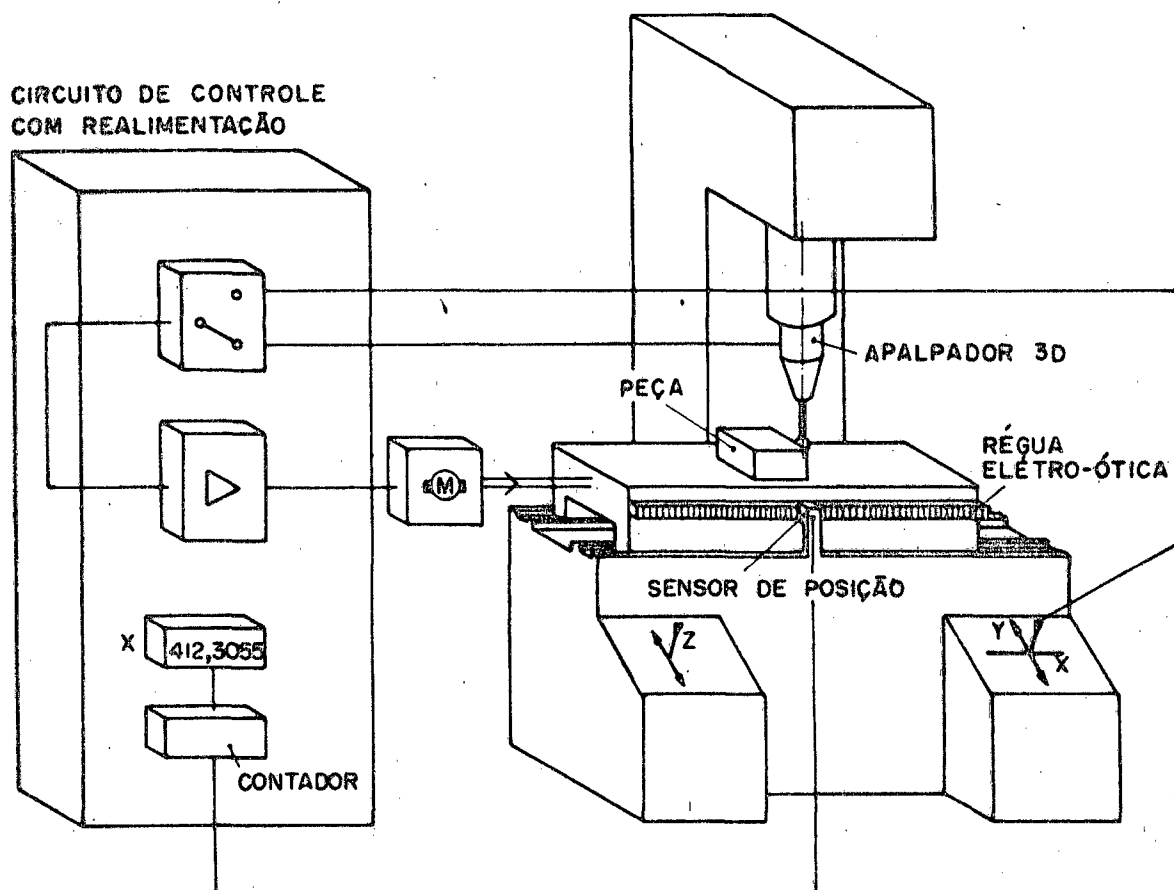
Máquina de medição 3D com sistema de leitura automático [7].
